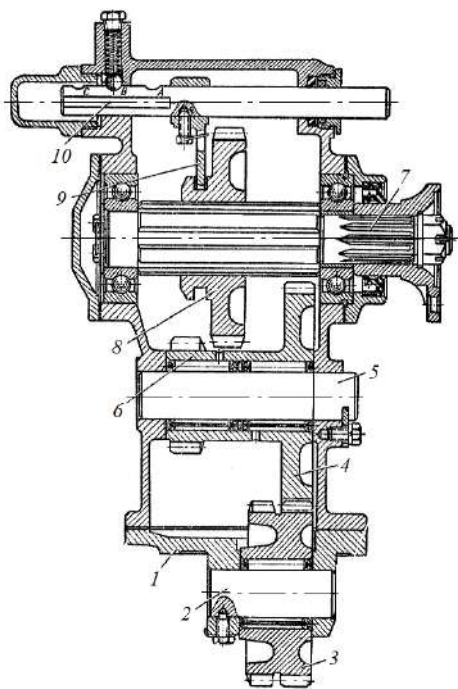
Коробка відбору потужності з редуктором:
